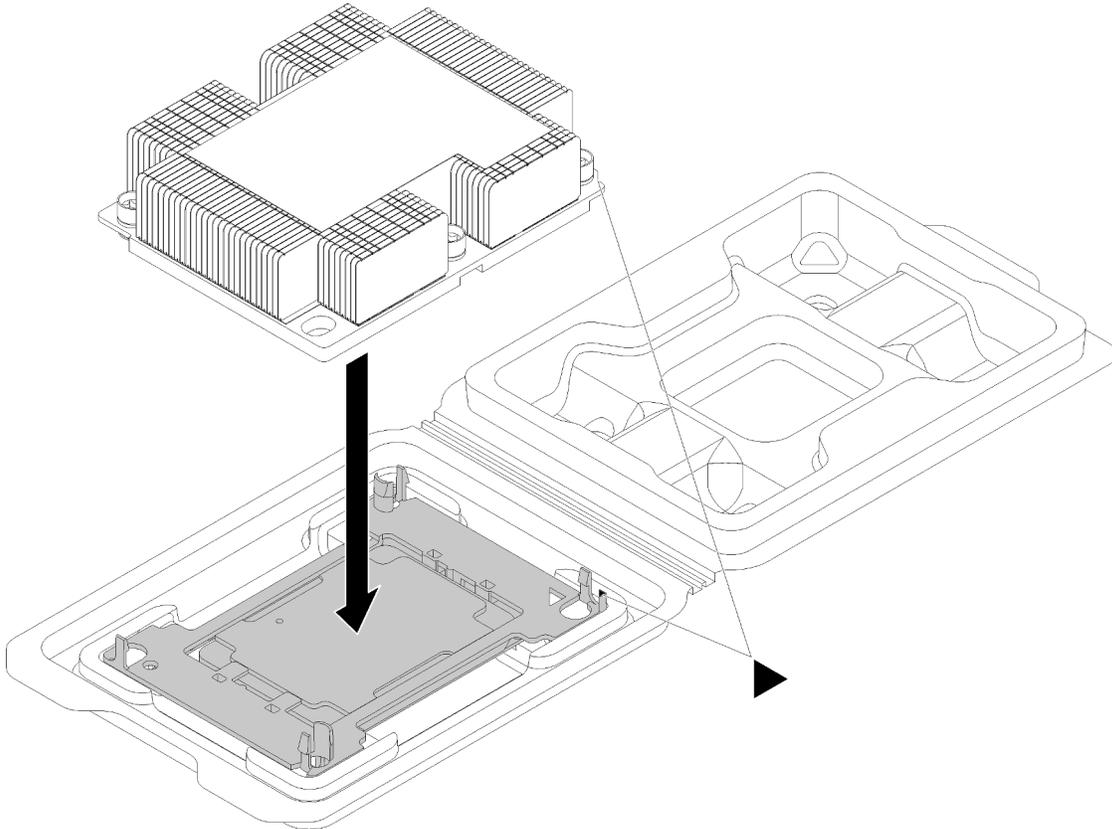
Assemblaggio di un dissipatore di calore (PHM) nella confezione di spedizione
